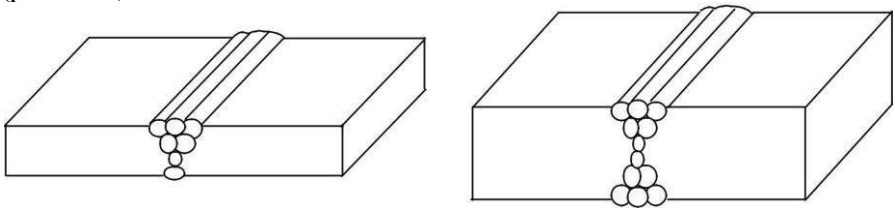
Формування швів при зварюванні пластмасових деталей
